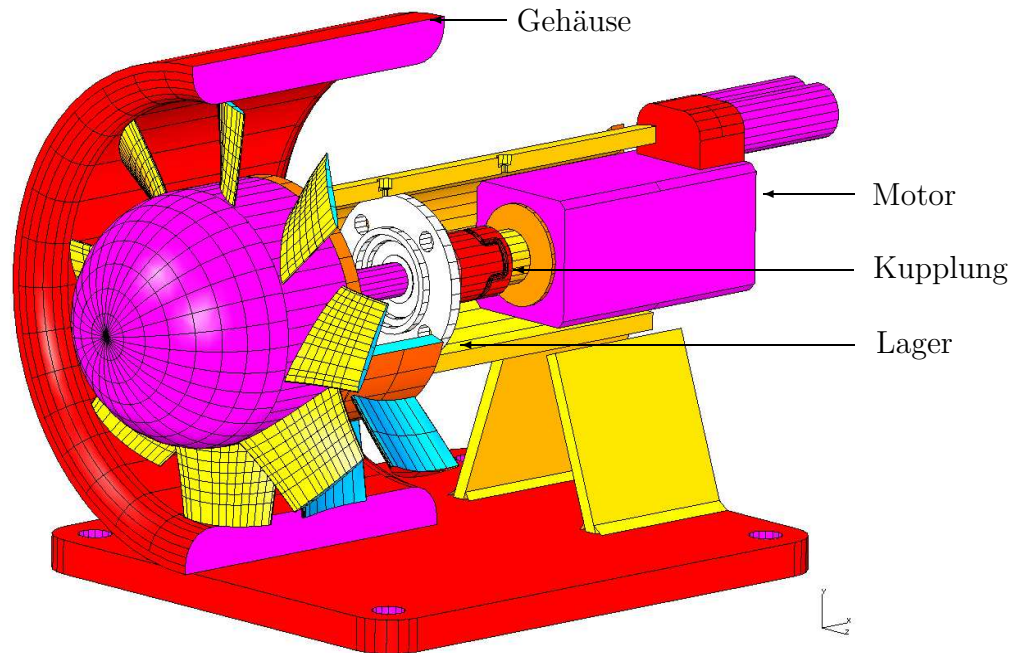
Prüfmaschine Ansicht von rechts (Schnitt)
